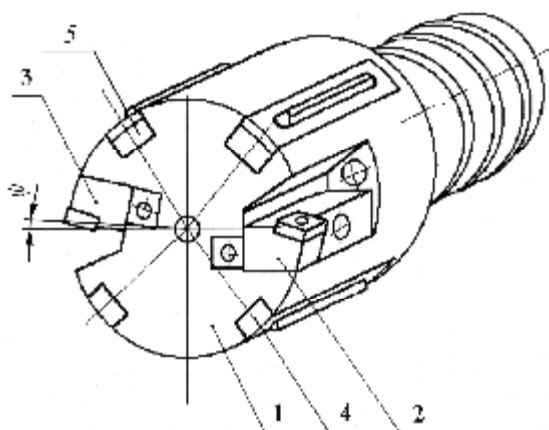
Виброустойчивая конструкция двухрезцовой расточной головки с угловым смещением резцовых блоков
